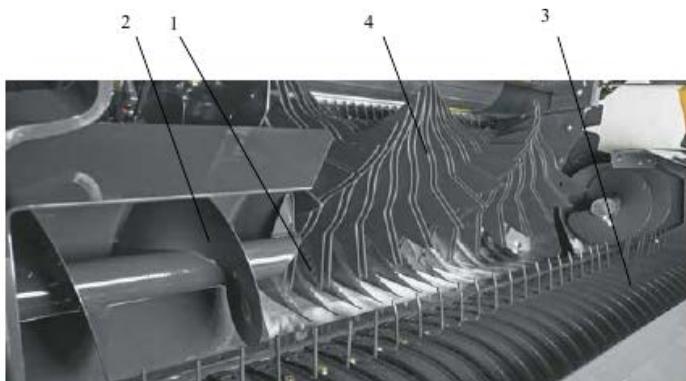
Захватывающий ротор: 1 – нож; 2 – шнек; 3 – подборщик; 4 – ротор
